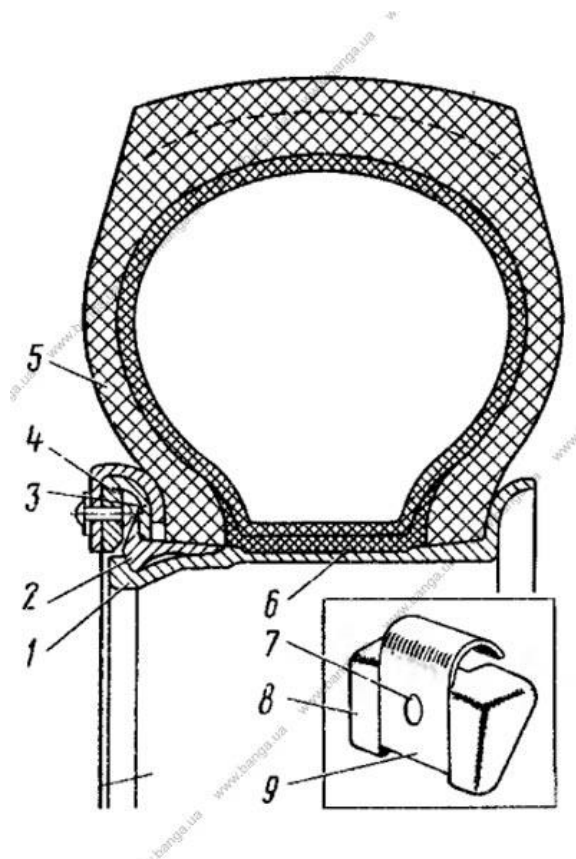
Колесо з балансувальними вантажами: 1-обід колеса; 2-кільце замочне; 3-кільце бортове; 4-вантаж балансувальний у зборі; 5-шина; 6-обідня стрічка; 7-заклепка; 8- вантаж балансувальний; 9-пружина
